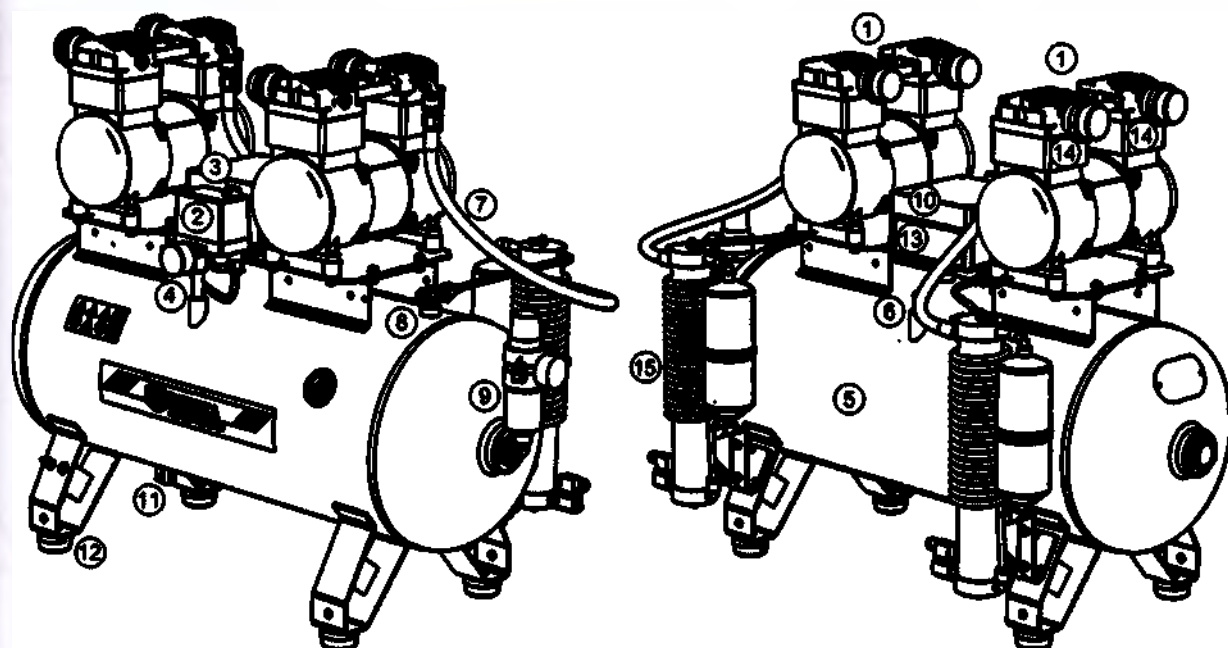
Общий вид компрессора KM-100.OLD15TD и KM-100.OLD20TD
